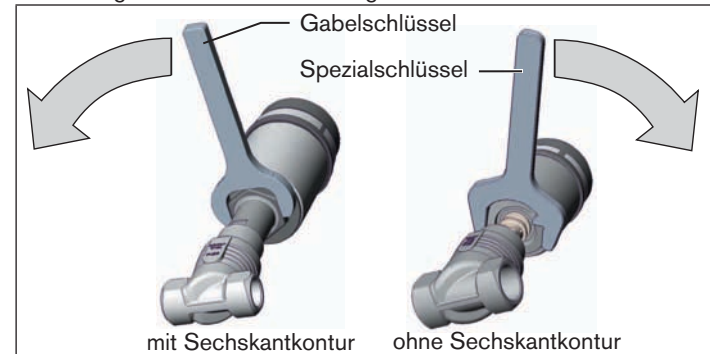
Drehen mit Gabelschlüssel / Spezialschlüssel
